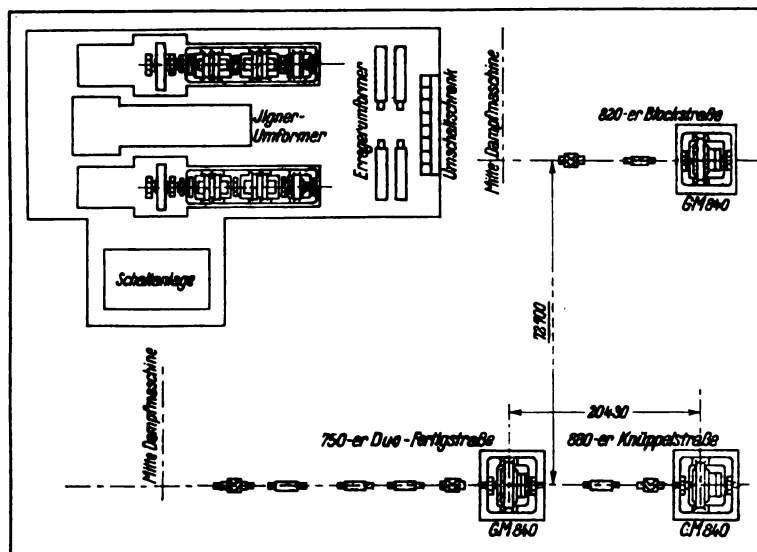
Lageplan der schwungradlosen Walzenstraßen.
